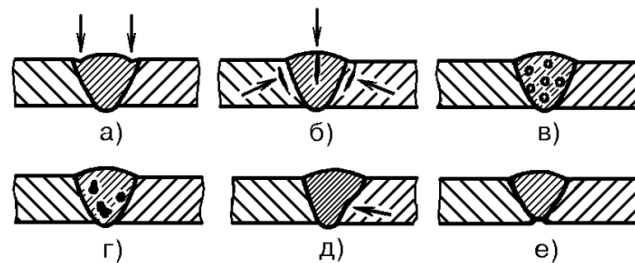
Поперечні перерізи зварювальних швів із типовими дефектами
